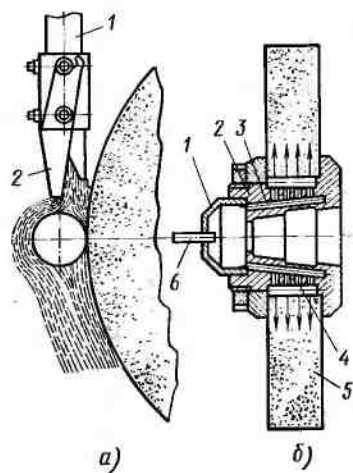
Конструкции устройств для подачи СОЖ:
